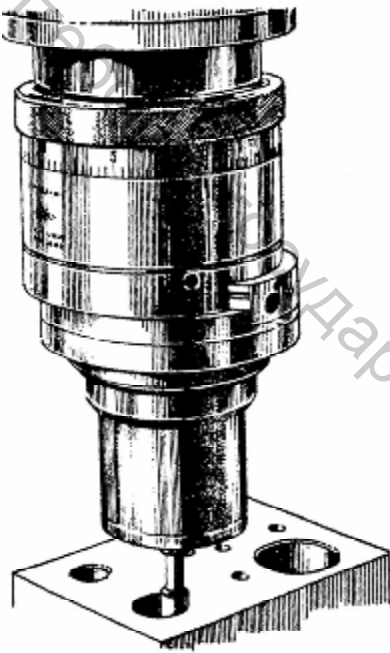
Планетарный шпиндель со шлифовальной головкой
